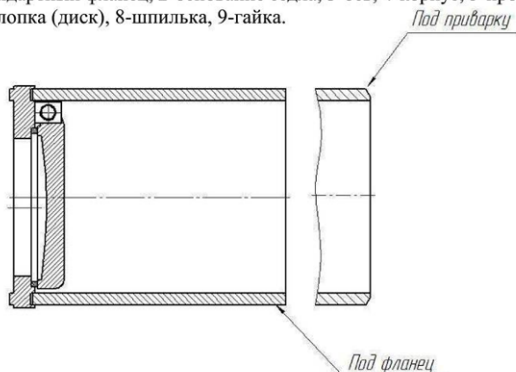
Вариант изготовления затвора без фланцев и с концами под приварку
